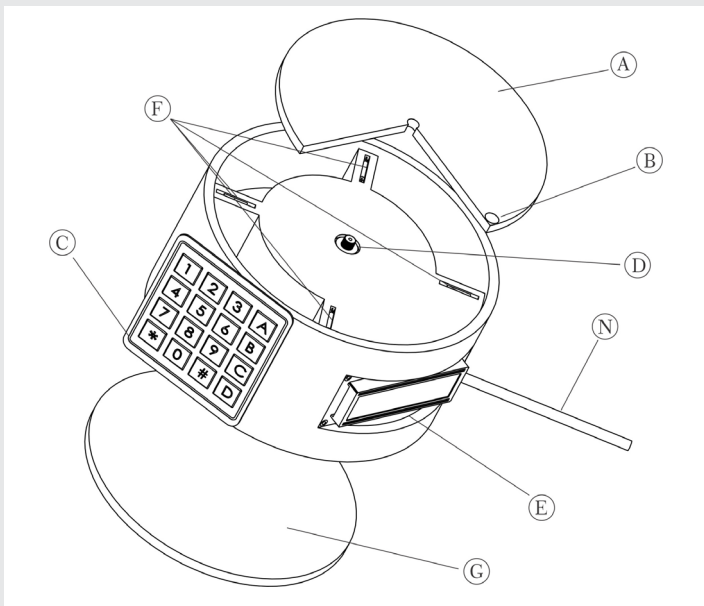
Descomposición detallada del dispositivo diseñado en SolidWorks.
